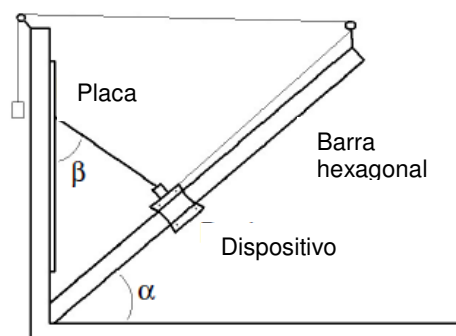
Sistema de soldadura gravitacional vertical [25].
